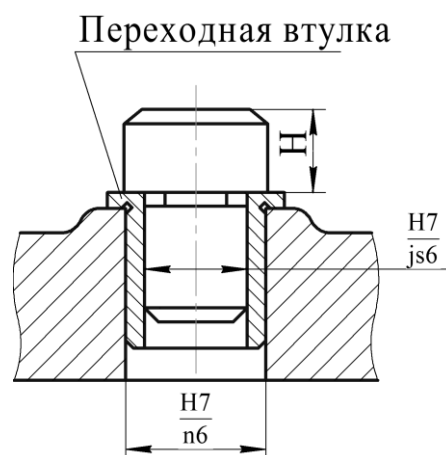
Установка штыря в корпус с использованием переходной втулки
